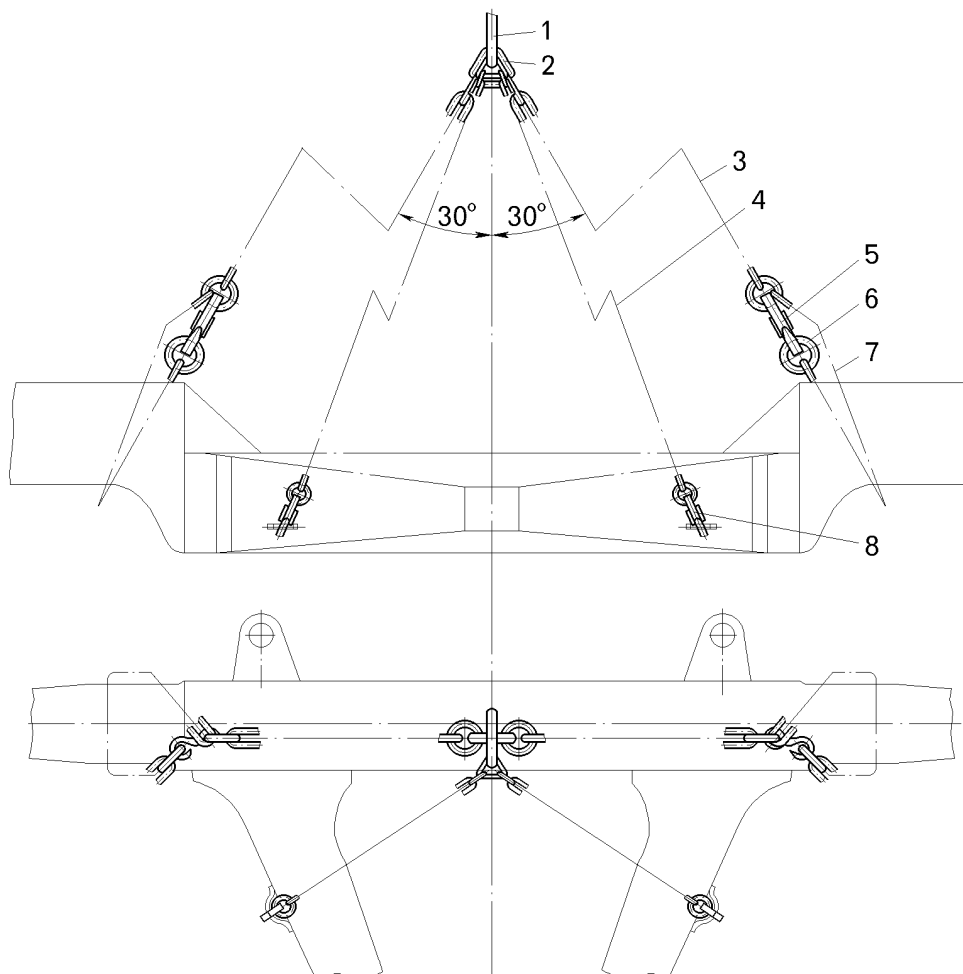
Чалочное приспособление для зачаливания передней оси:
